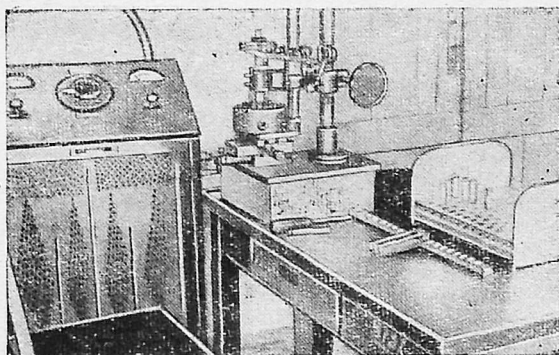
Станок для трубчатых соединений стекла с металлом с нагревом током высокой частоты. Общий вид.
